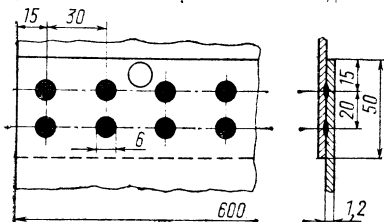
Шов двухрядной точечной сварки, шахматный
